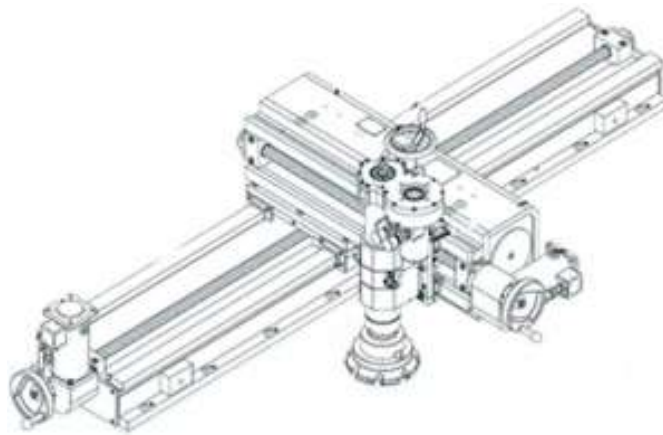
Приклад конструкції портативного фрезерного обладнання
